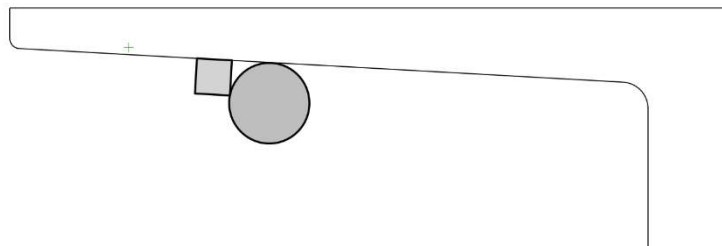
Detalle de la posición de un rodillo sobre la barra soldada al perfil UPN. Croquis.
